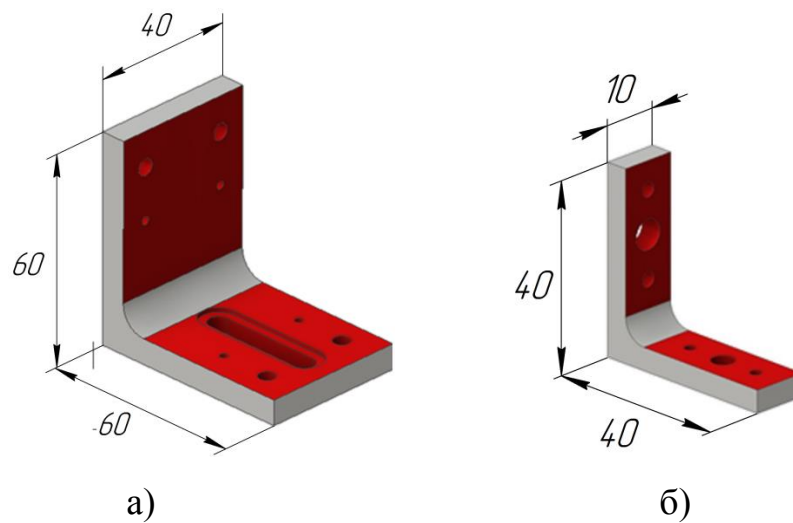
Деталь типу кронштейни для оброблення на багатокординатному фрезерному верстаті
